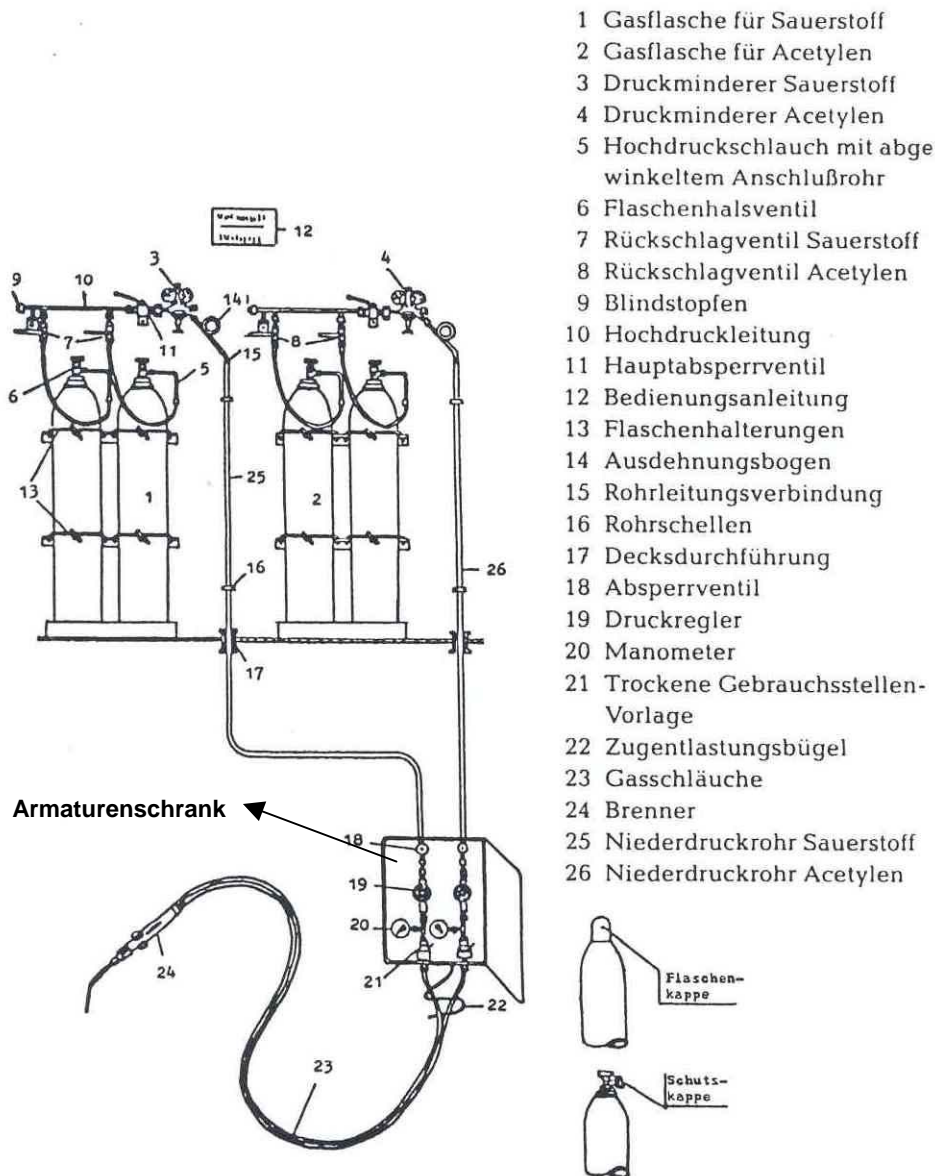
Aufbau der Gasschweißanlage<sup>2</sup>
